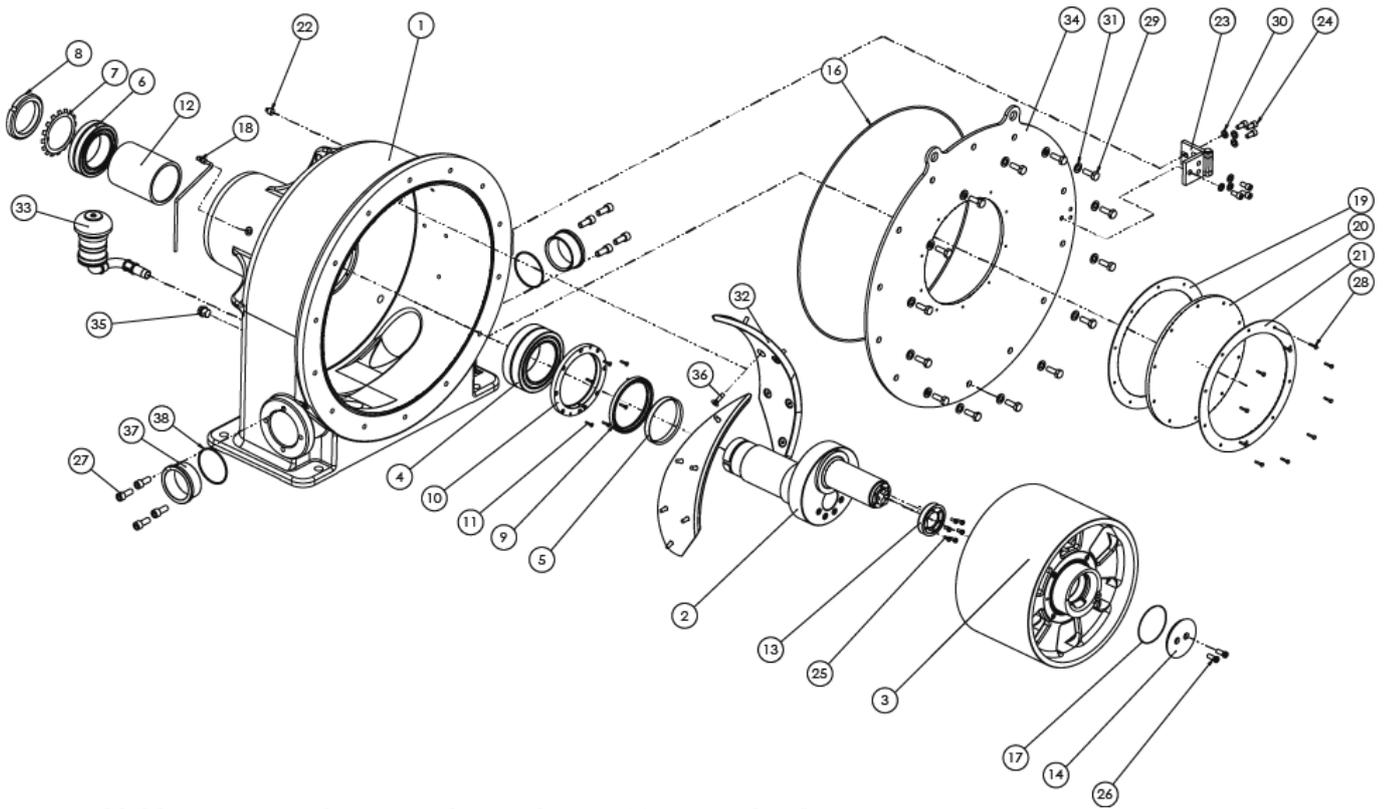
Explosionszeichnung des LPP-T-Pumpenkopfs
